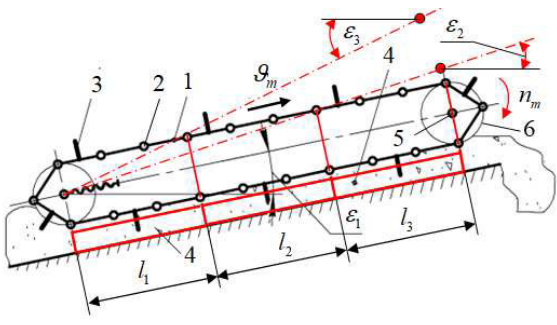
Схема похилого транспортера: 1 – робоча гілка транспортера; 2 – пруток; 3 – скребок; 4 – ємність; 5 – ведучий вал; 6 – привідна зірочка
